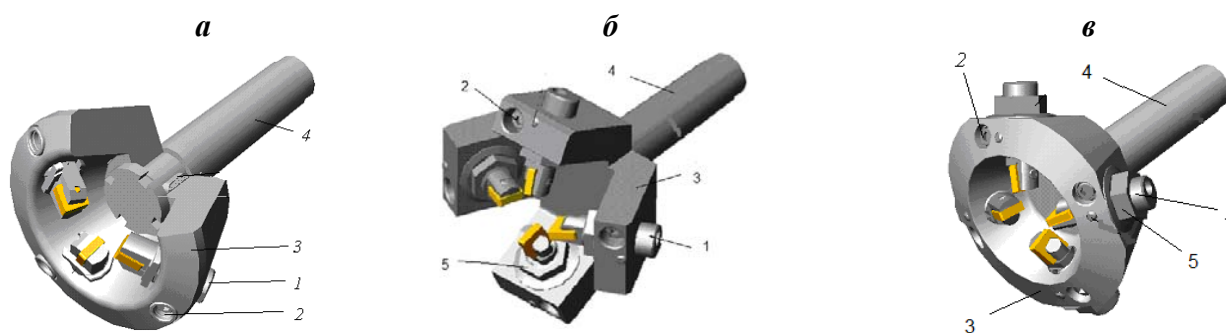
Конструкции фрез для высокоскоростной обработки сферических поверхностей:
